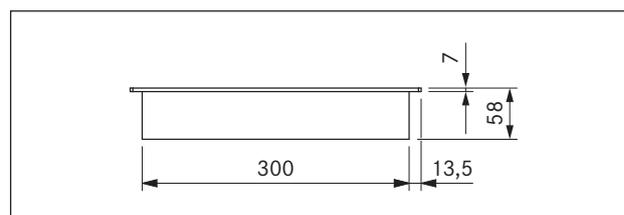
Dimensões do aparelho CKFI, vista frontal
